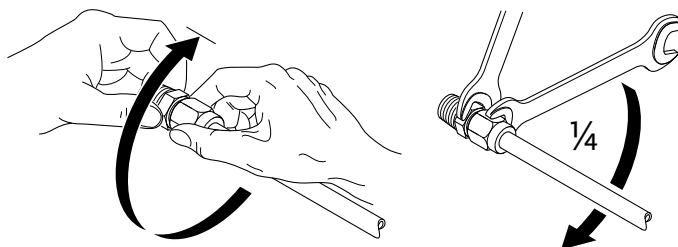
1/4 de rotação adicional da abraçadeira de ligação
